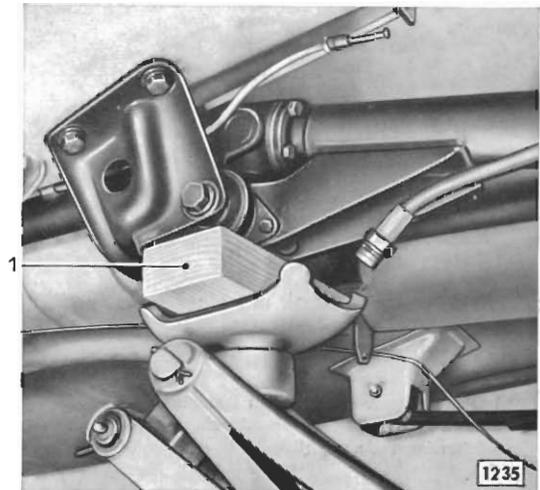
Hinterachsgelenk zum Abschrauben der Gelenkbrücke mit Wagenheber abgestützt
